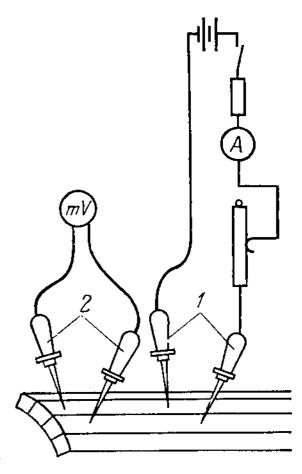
Схема для проверки соединений обмотки якоря машины:
